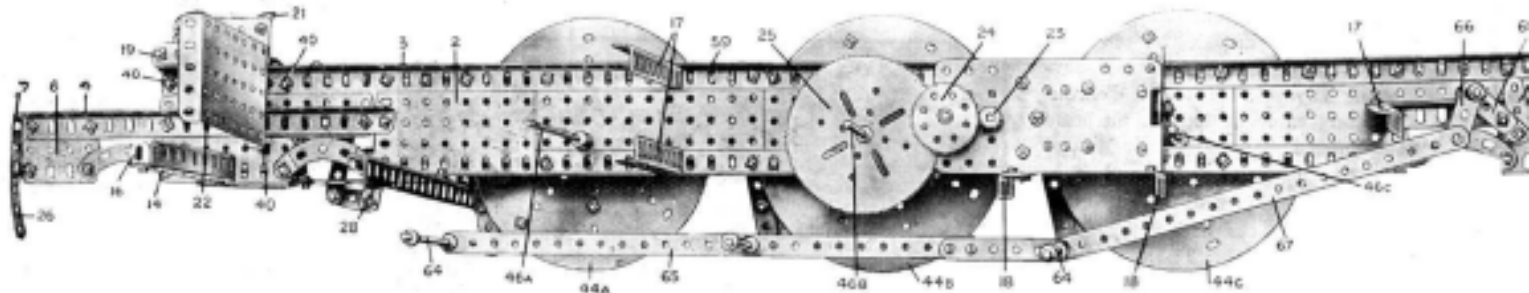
Vue intérieure du côté droit du châssis montrant la position du Moteur et des Engrenages démultiplicateurs.
